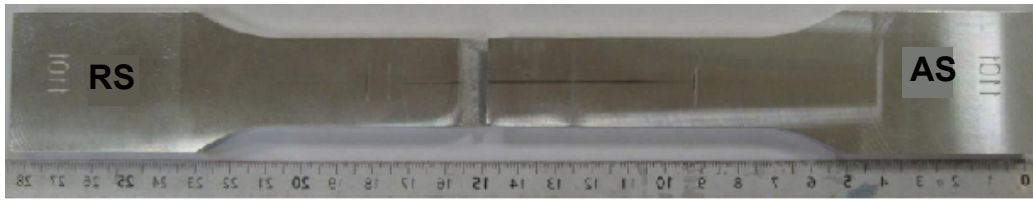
Rupture des joints soudés par FSW en alliage d’aluminium 2050-T851 sous chargement de traction monotone quasi-statique
